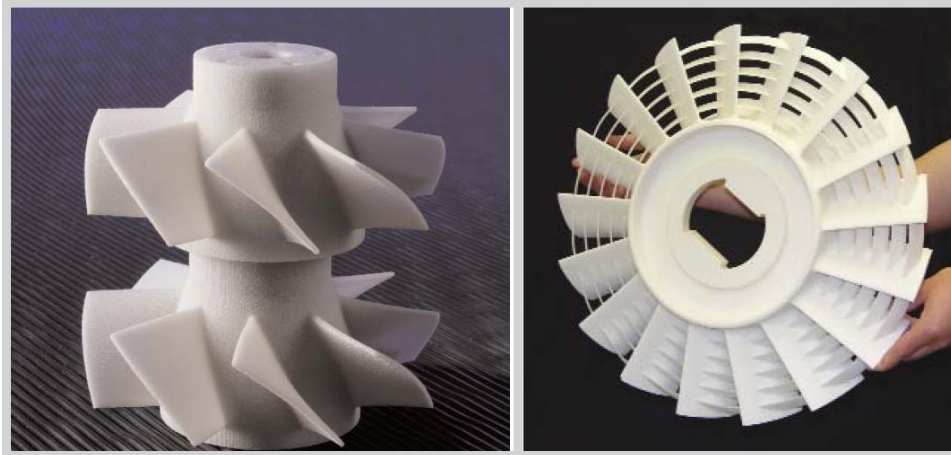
Piese din DURAFORM PA/ Figure 1. Parts of DURAFORM PA
